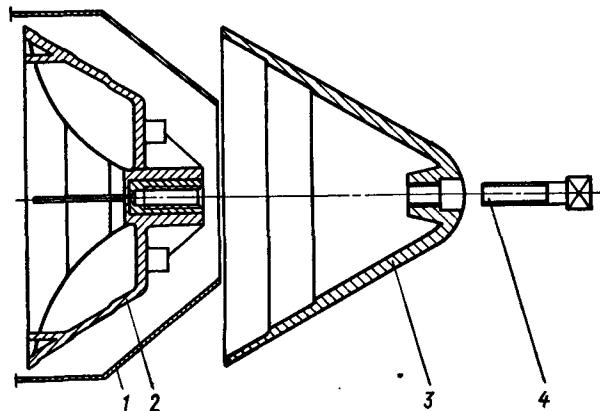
Заделка кормовой эластичной оболочки двумя стягивающими коническими деталями
